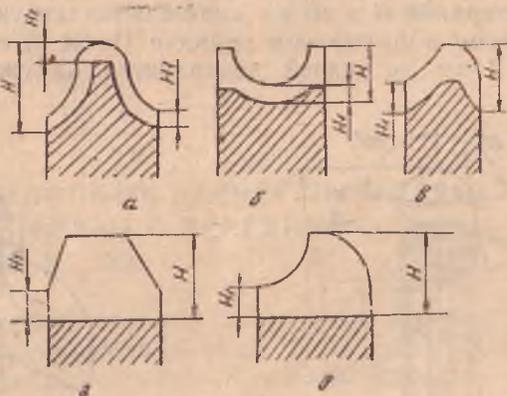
Согласование дна стружечной канавки с формой профиля зуба
